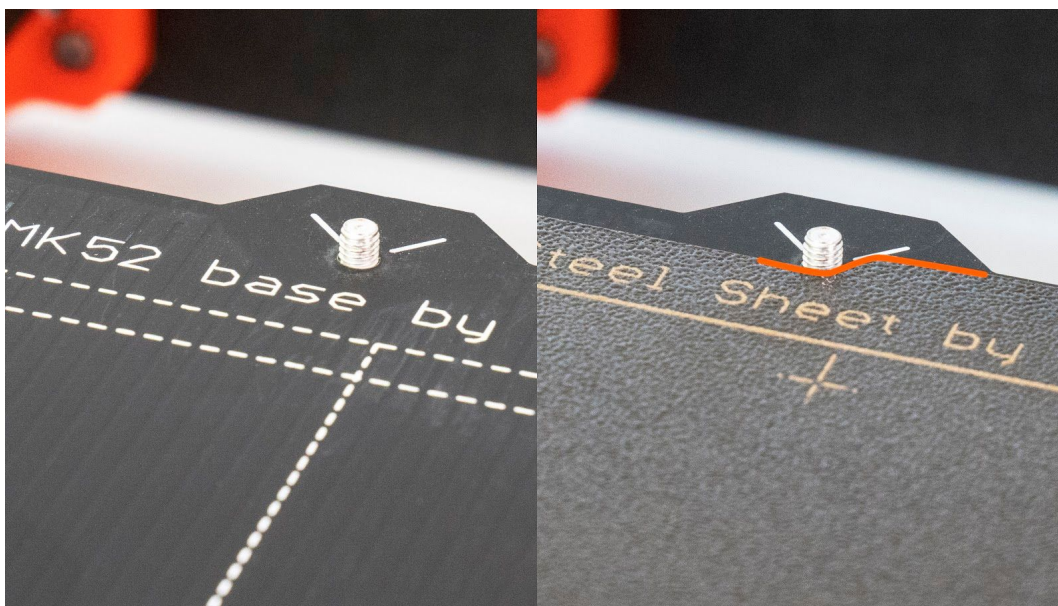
Base calefactada MK52 y plancha de acero con superficie recubierta de polvo
